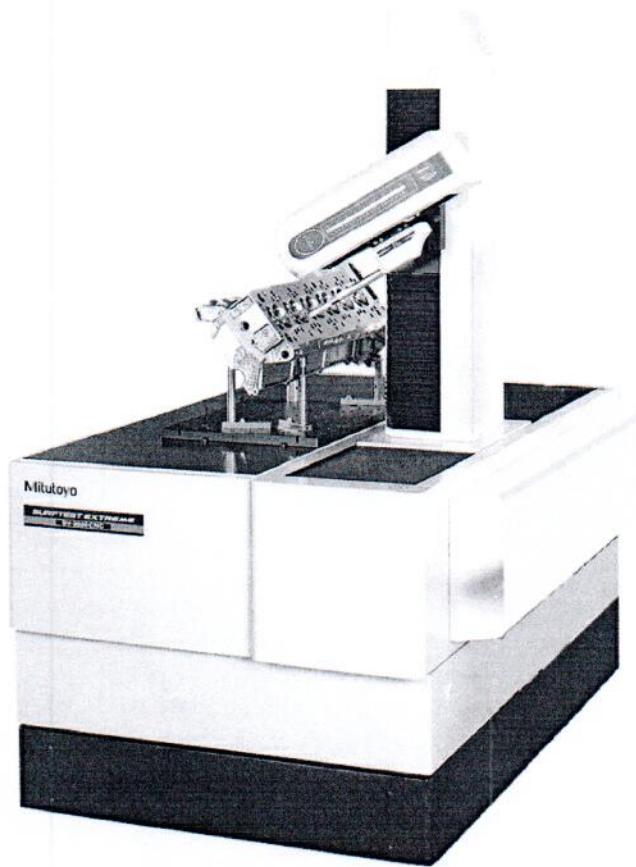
Внешний вид приборов для измерения параметров шероховатости
